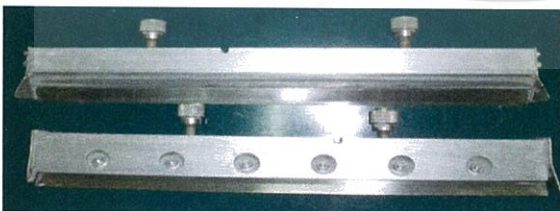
Solder Paste Printing Vender คือ HITACHI
